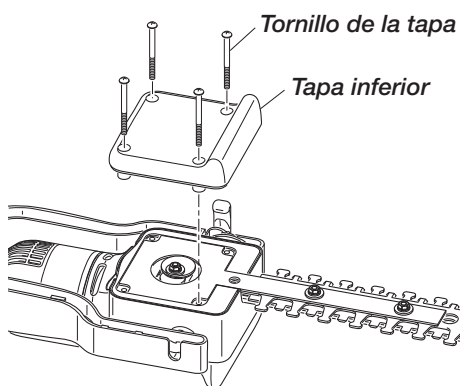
Retiro de la tapa inferior de la cabeza de la podadora
